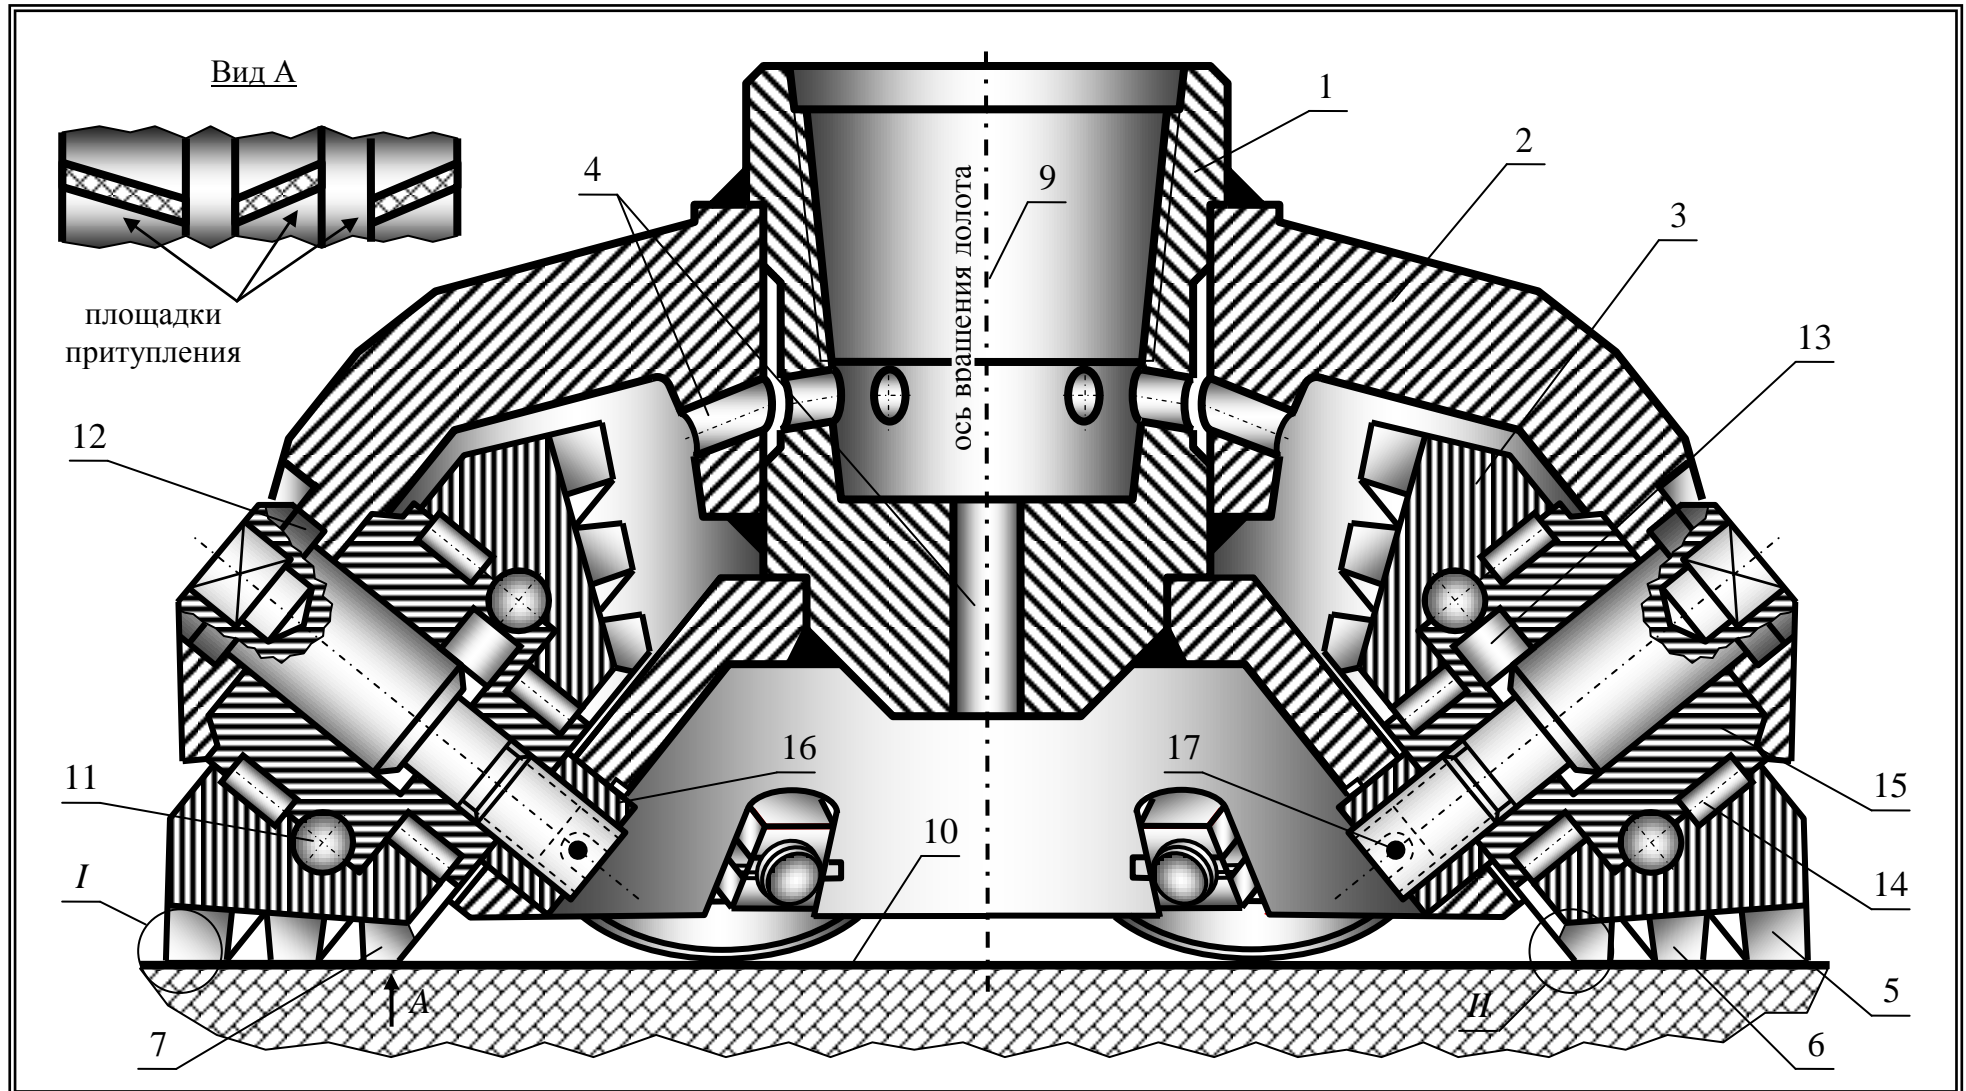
Шестишарошечное долото со сменными шарошками: 1-корпус; 2-лапа; 3-шарошка; 4-канал промывки; 5-калибрующий венец; 6-основной венец; 7-вершинный венец; 9-ось вращения долота; 10-поверхность забоя; 11-шарик; 12-ось шарошки; 13-палец; 14-ролик; 15-цапфа; 16-втулка; 17-шплинт.
